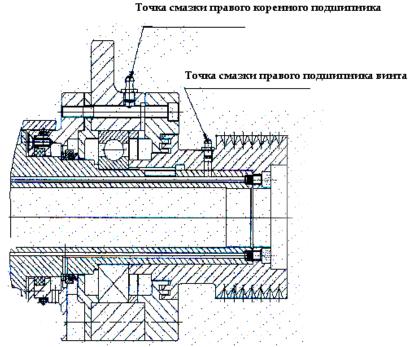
Смазка правого подшипника и правого коренного подшипника
